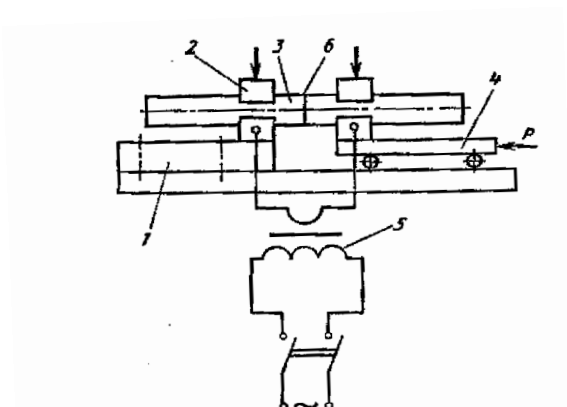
Схема контактной стыковой сварки:1 - неподвижная плита; 2 - зажимы (электроды); 3 - заготовка; 4 подвижная плита; 5 - сварочный трансформатор; 6 – контакт.
